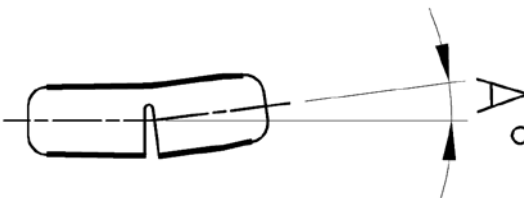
Общий вид верхней выравнивающей пластины.
